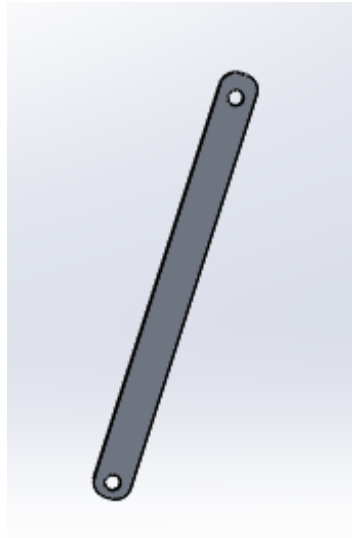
Dimensión de la pieza apoyo del pie
